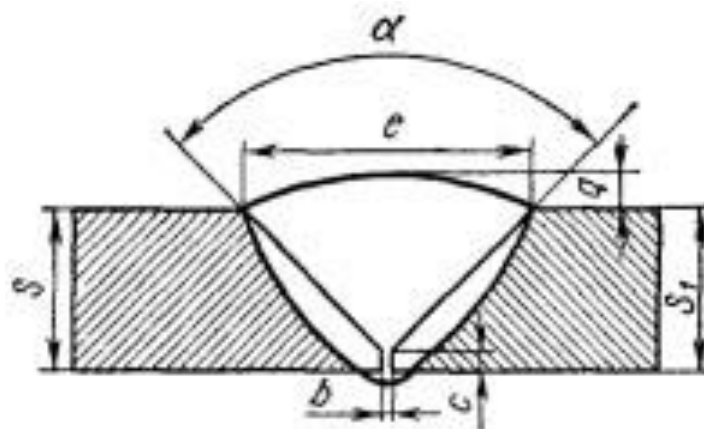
1 – Сечение сварного шва с разделкой кромок
